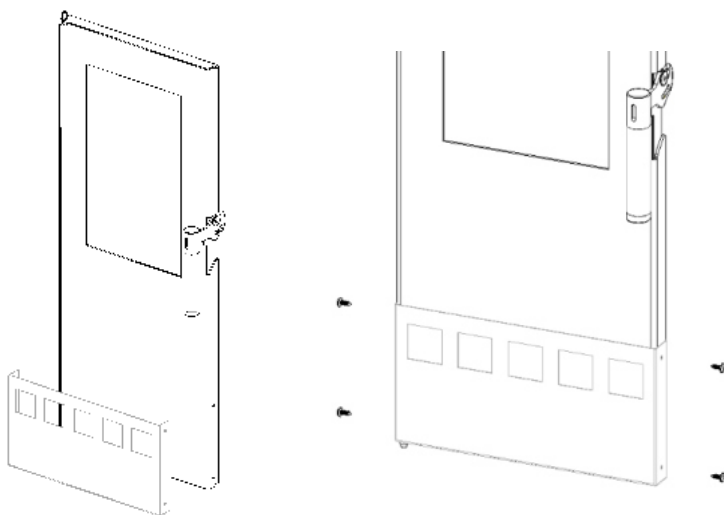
Instrucciones para aplicar la puerta tapa frontal
